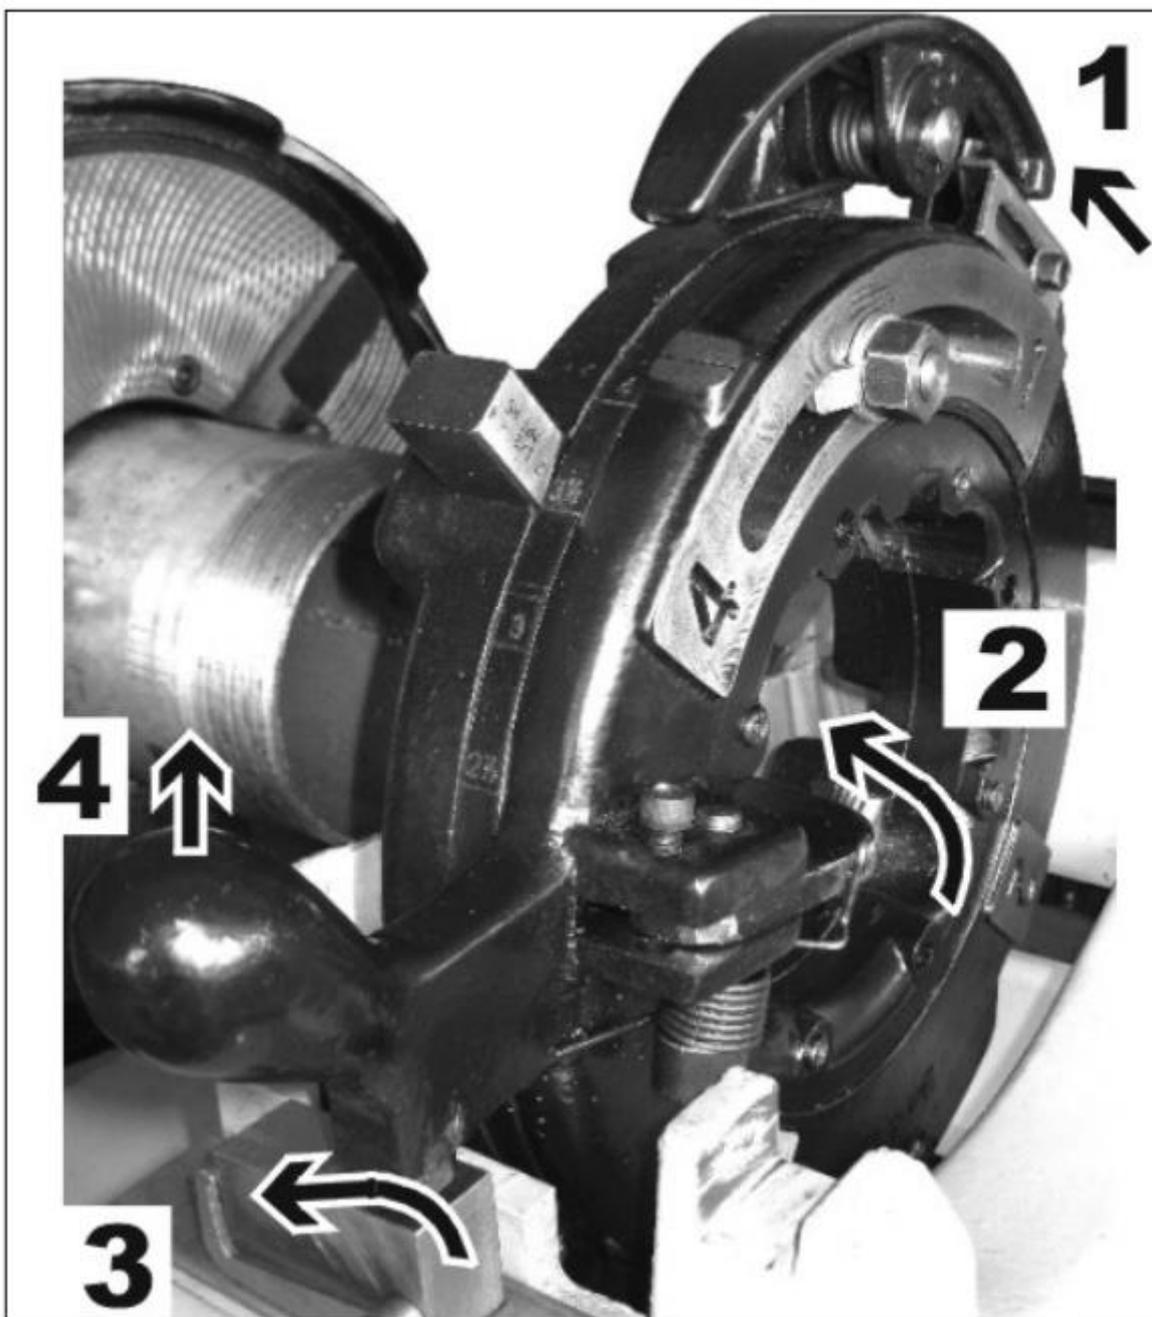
Установка 2 1/2"-4" резьбонарезной головки для нарезания NPT или BSPT резьбы
